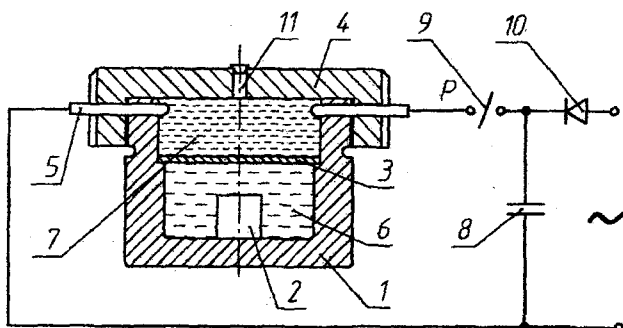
Схема процесса электрогидравлической штамповки: 1 – корпус; 2 – штампуемая заготовка; 3 – мембрана; 4 – крышка с каналом 11 для залива воды, со шлицами, чтобы завернуть ее по резьбе; 5 – электроды; 6 – жидкость, осуществляющая штамповку; 7 – вода, в которой происходит электрический разряд; 8 – конденсаторная батарея; 9 – разрядник; 10 – выпрямитель электрического тока; 12 – заглушка
